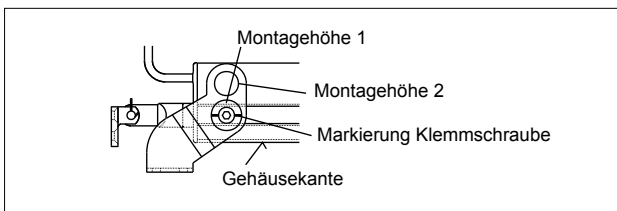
Abb.D.: Markierung Klemmschraube parallel zur Gehäusekante
